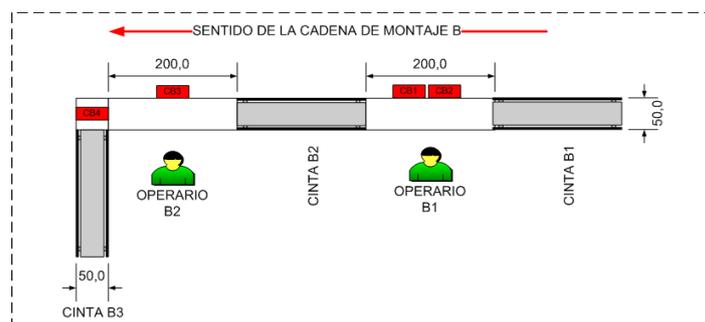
Diagrama de planta de la Cadena de Montaje B (cotas en cm).
